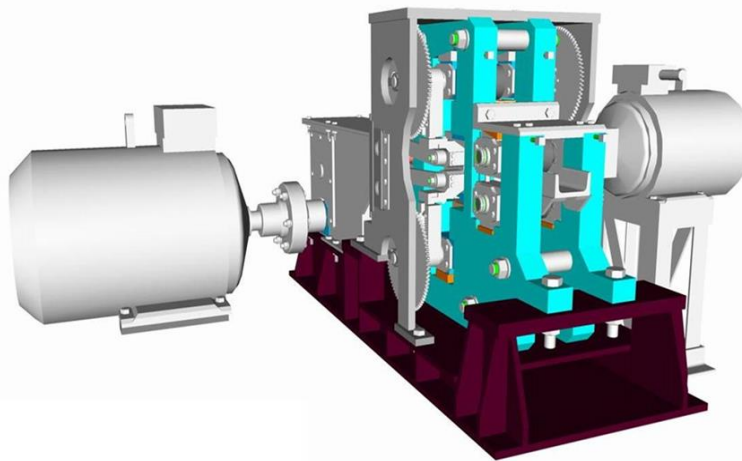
Общий вид лабораторного маятникового стана с цепным приводом
